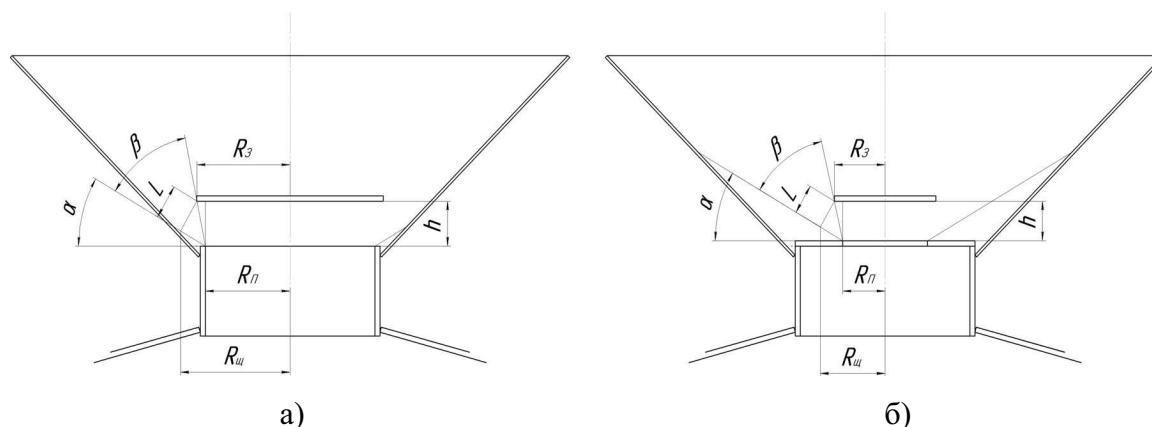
Расчётные схемы загрузочного устройства: а – без кольца; б – с промежуточным кольцом.
